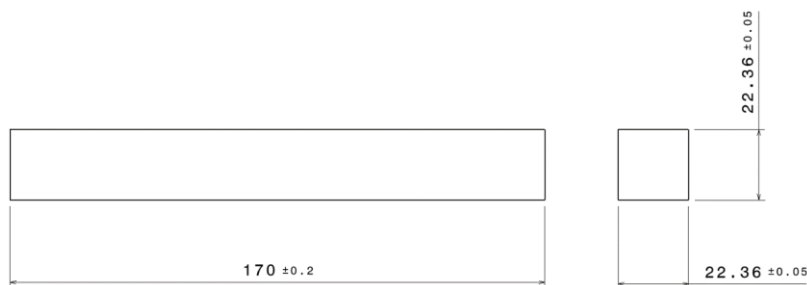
Dimensions de l'éprouvette de flexion
